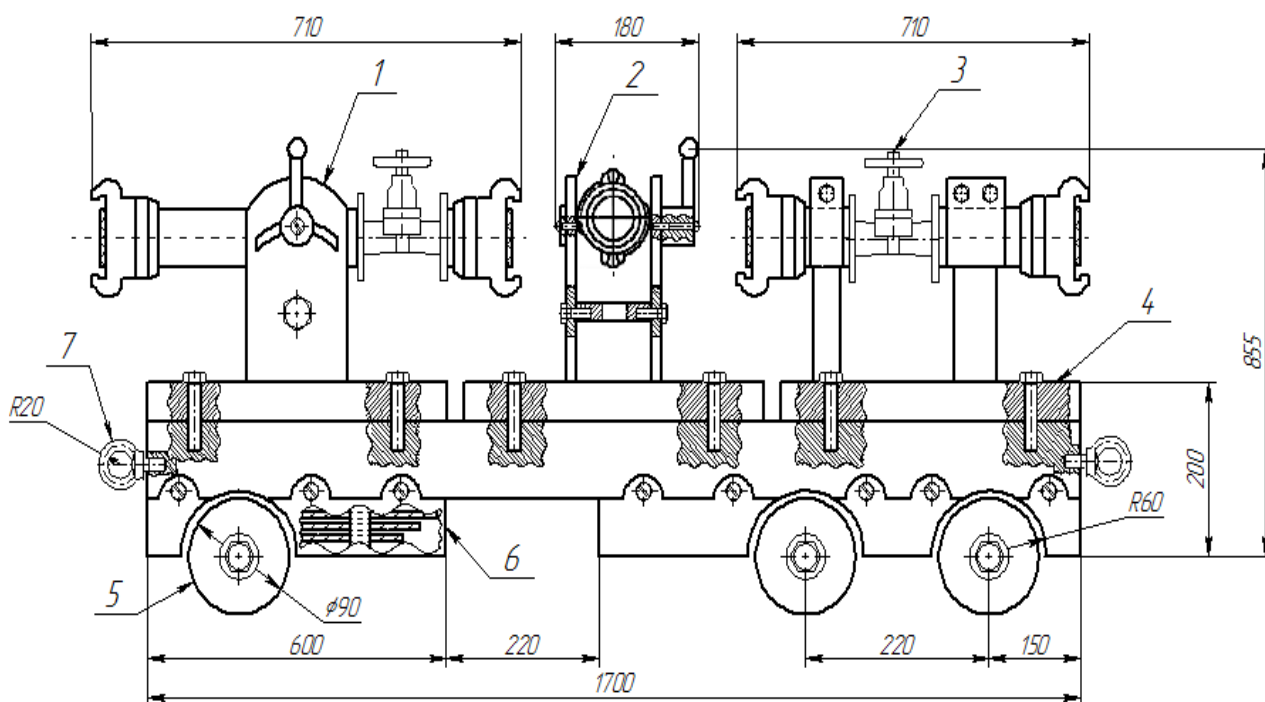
Сборочный чертёж устройства для дистанционного тушения возгораний
